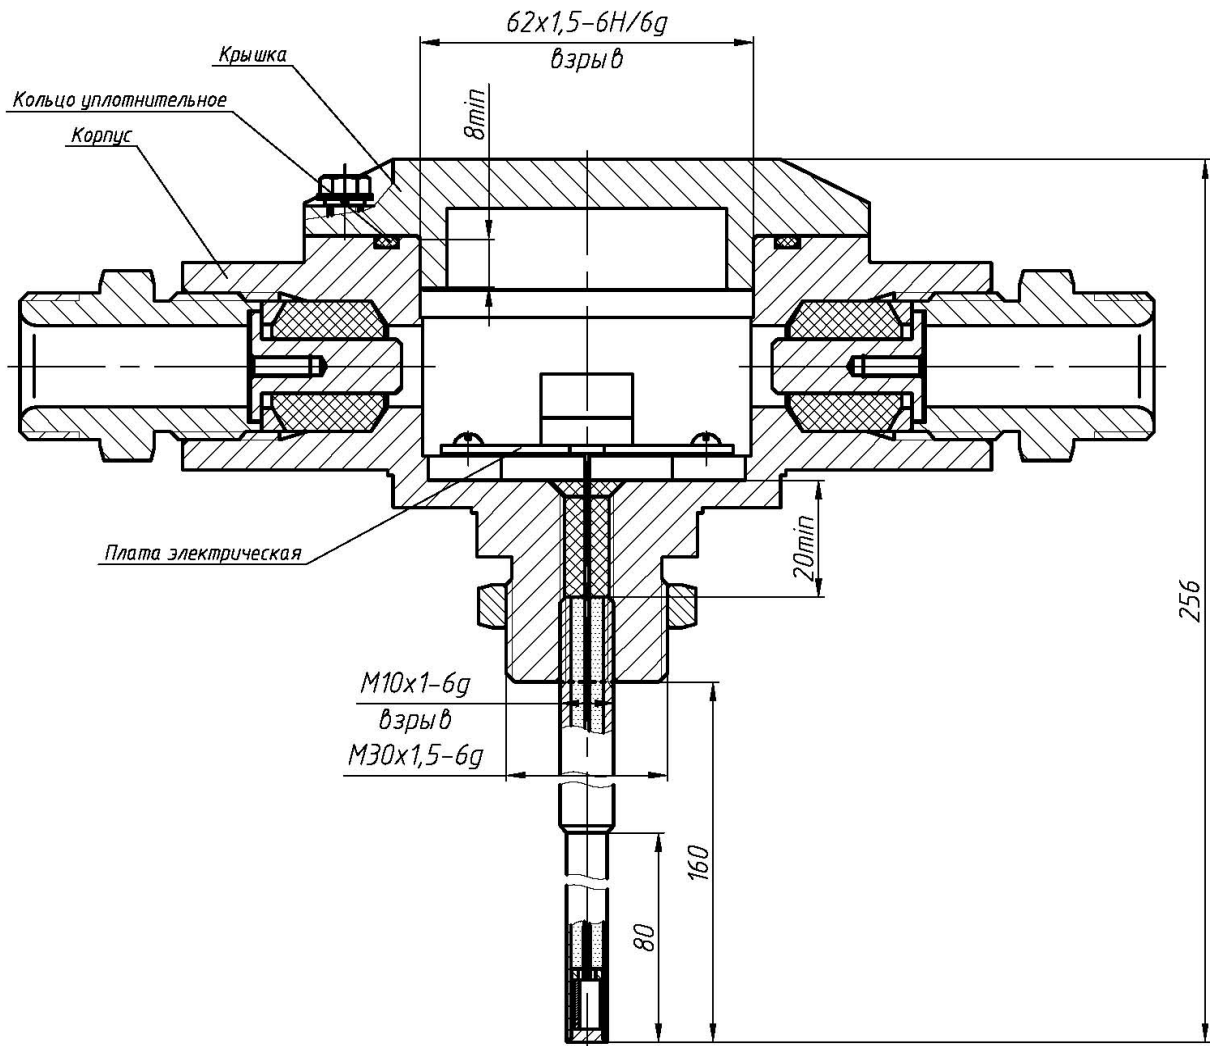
Габаритный чертёж ИП103-2В/П-А в алюминиевом корпусе
